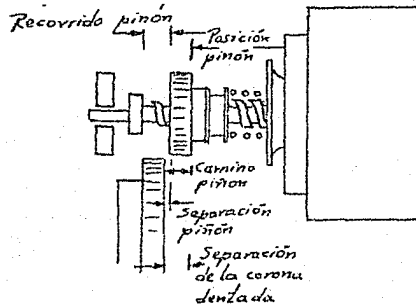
Ajustes de posición del piñón y corona dentada.
